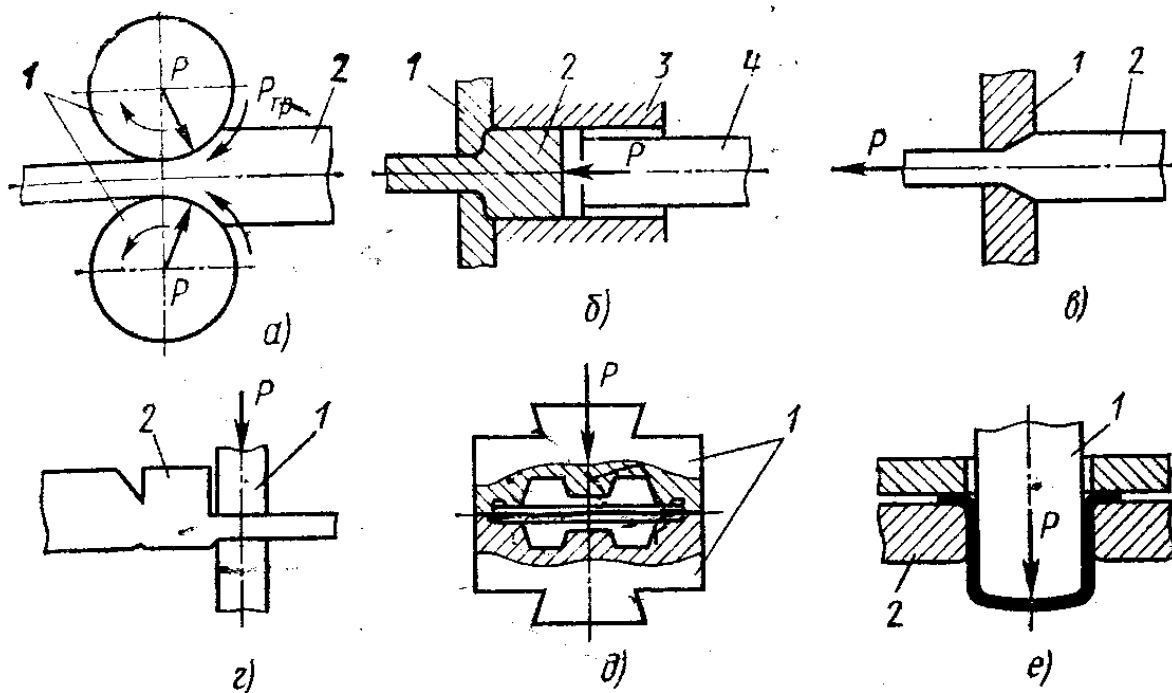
Схемы основных видов обработки металлов давлением для получения деталей или заготовок (полуфабрикатов), имеющих приблизительно формы и размеры готовых деталей и требующих обработки резанием лишь для придания им окончательных размеров и получения поверхности заданного качества; основными разновидностями таких процессов являются ковка и штамповка.
